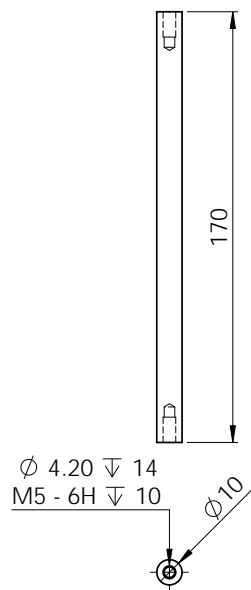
Technische Zeichnung der Stangen zwischen Bodenplatte und Ringaufsatz.
